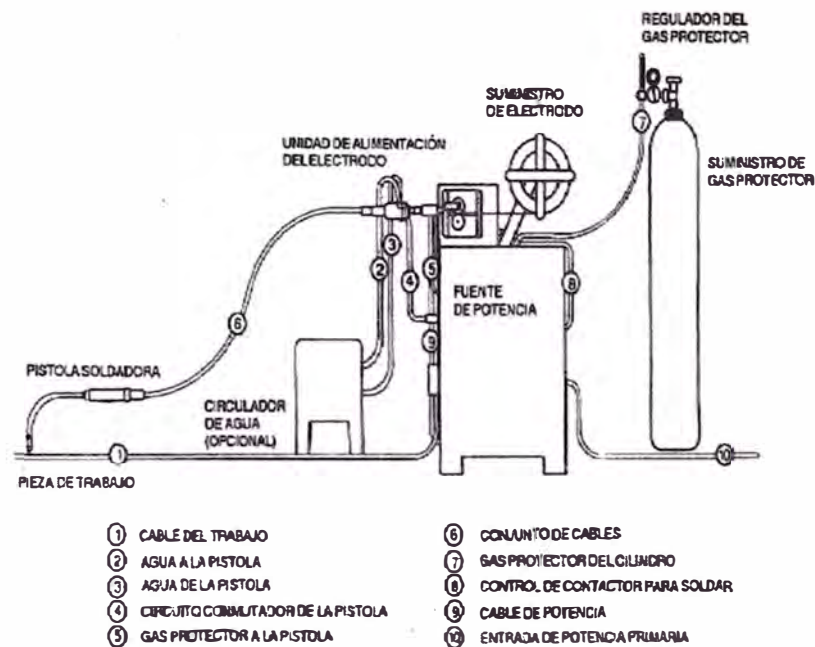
Proceso de soldadura por arco de metal y gas
